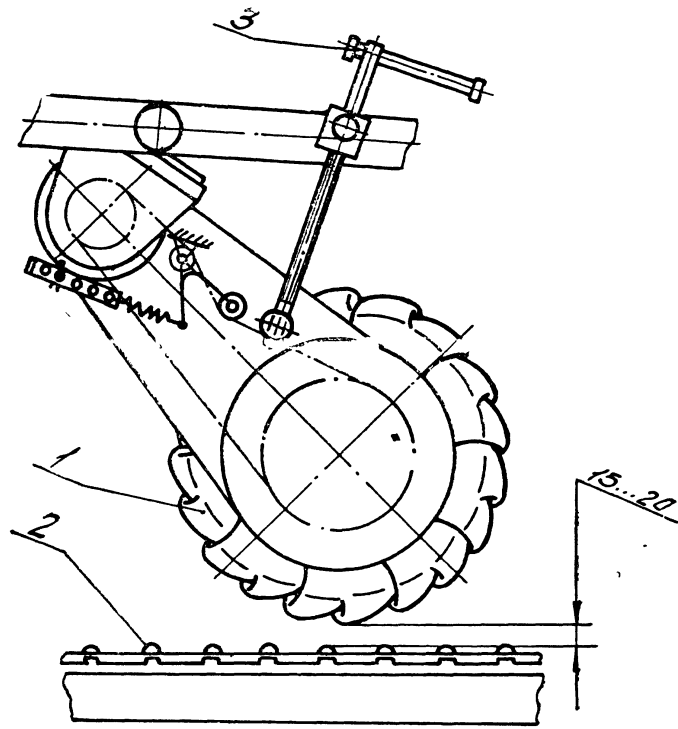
Регулировка интенсивности отделения примесей на основном элеваторе. Регулировка натяжения цепного контура: 1 – центральный шнек; 2 – прутки элеваторов; 3 – регулировочный винт
